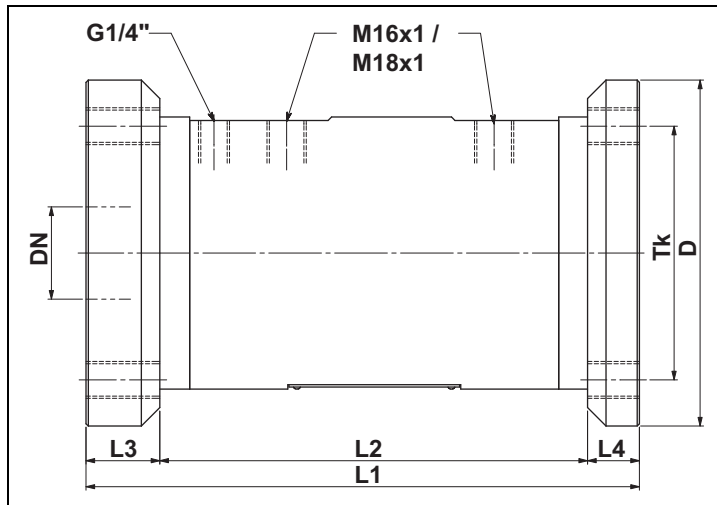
Maßzeichnung OMP mit Rohrgewinde
